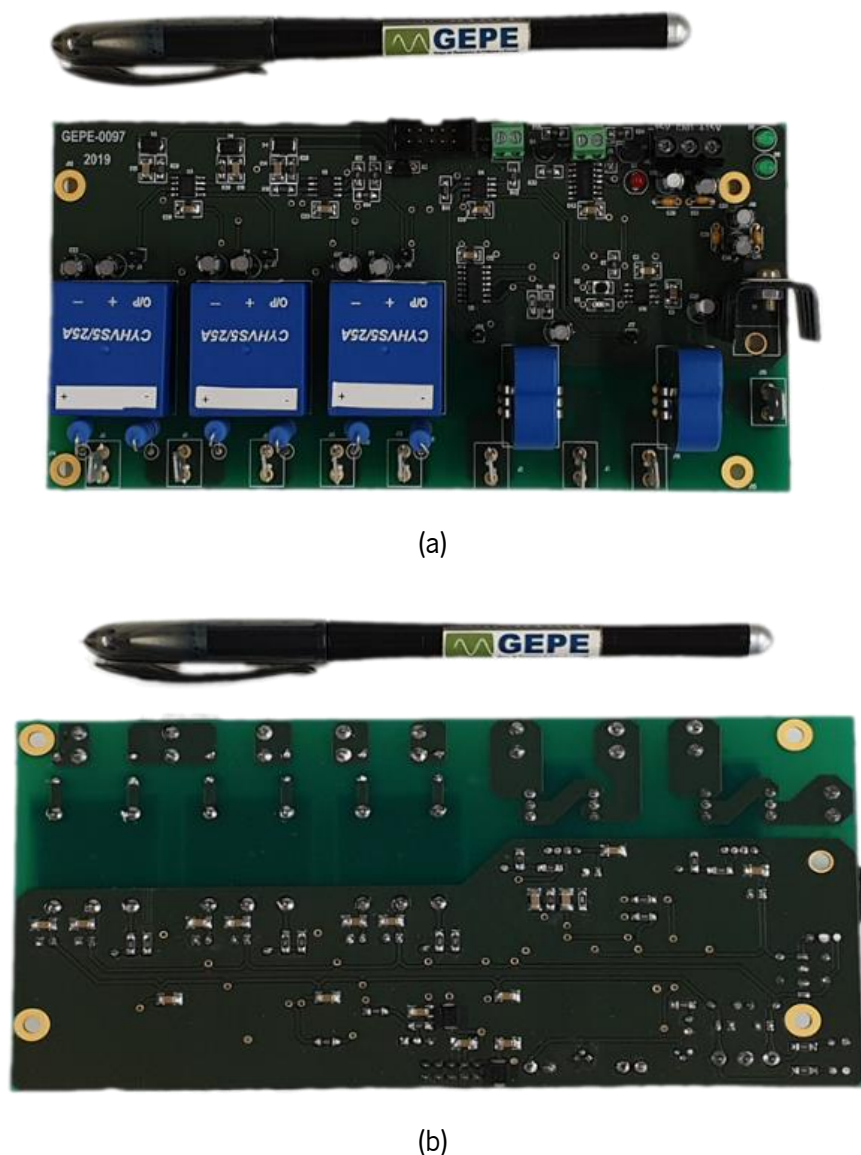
PCB desenvolvida com todos os componentes soldados: (a) *top* da PCB; (b) *bottom* da PCB.
